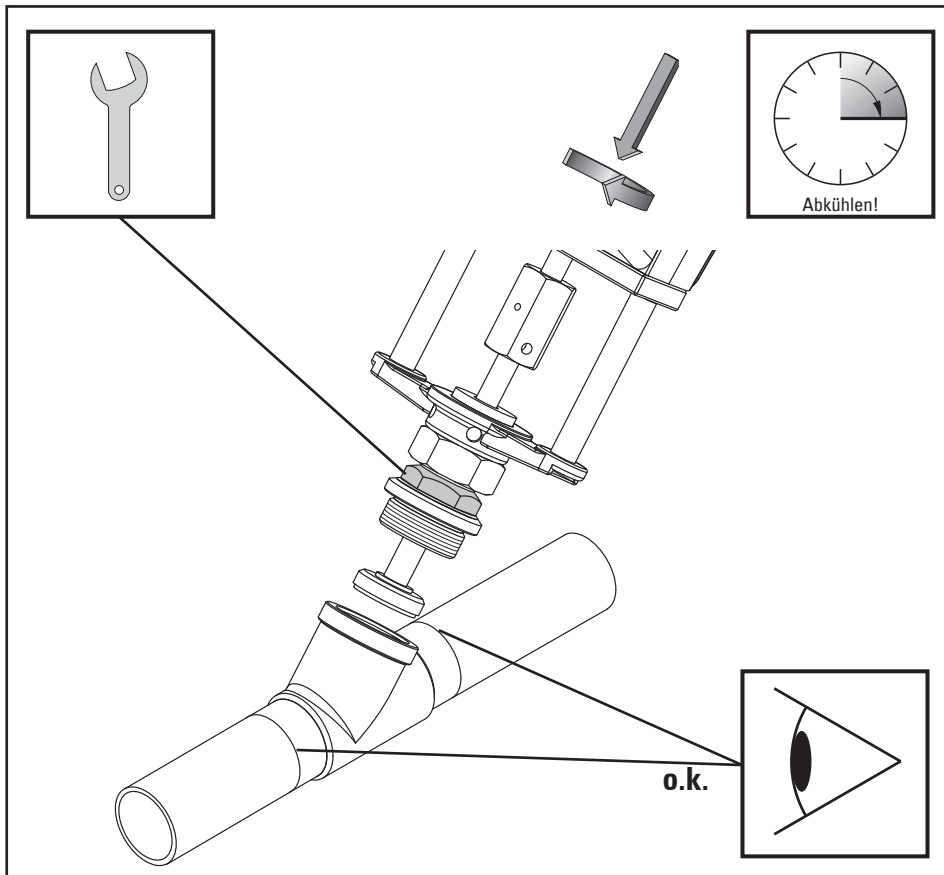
Montage des des Einschraubteils mit Antrieb
